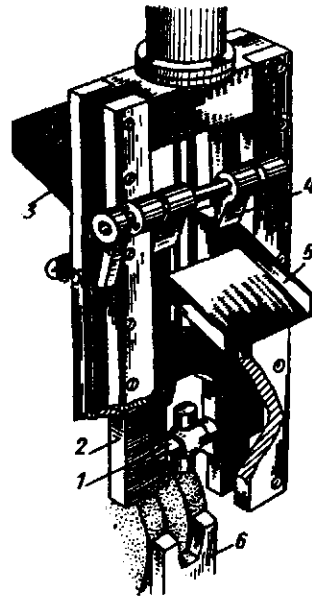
Схема автоматической загрузки деталей типа крестовины для шлифования двух разобраных шеек
